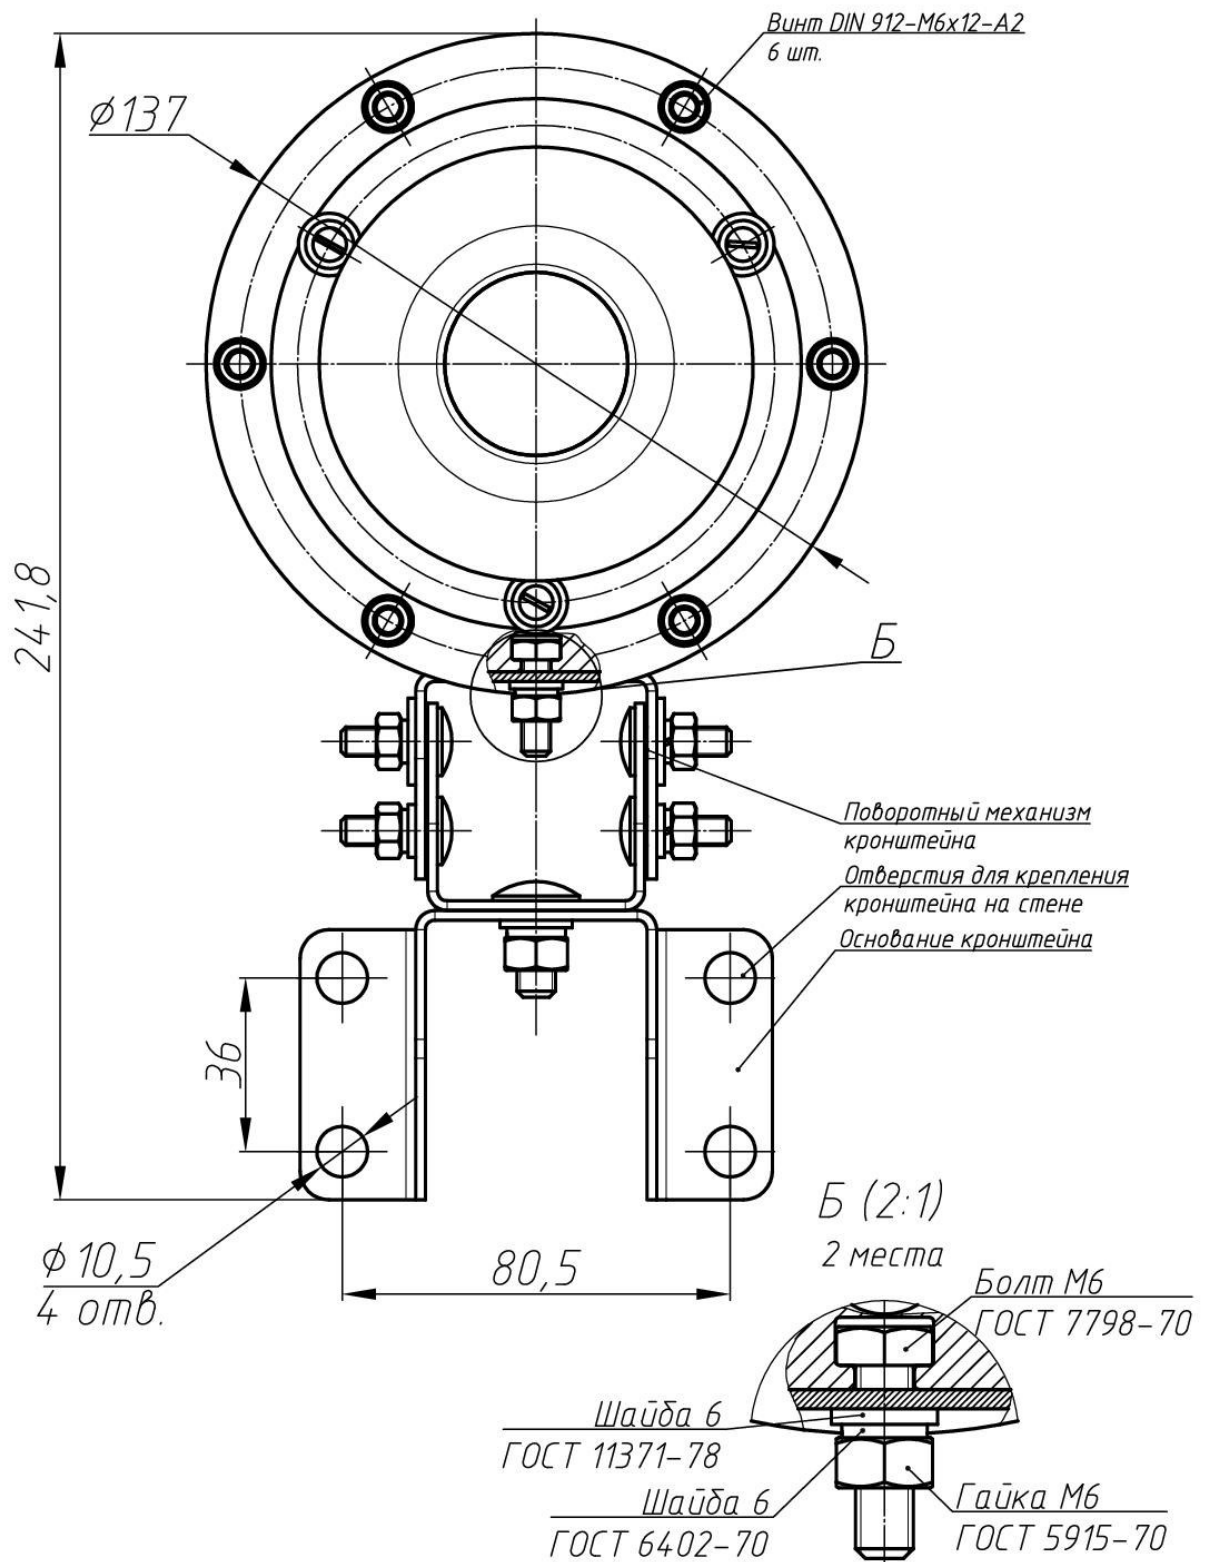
в - Габаритный чертёж громкоговорителя ГРВ-25А (вид сзади).
